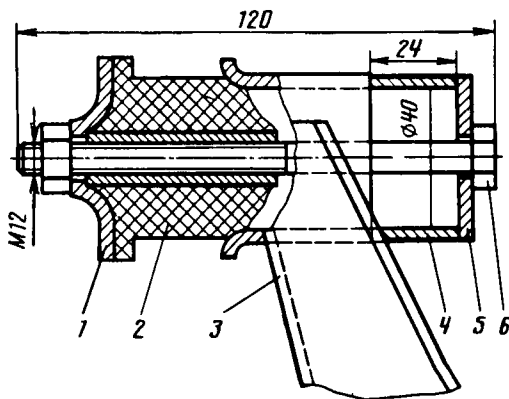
Запрессовка сайлент-блока в рычаг балки задней подвески:
